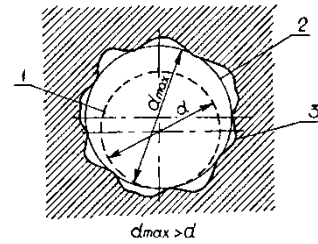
Прилегле коло для внутрішніх поверхонь обертання
